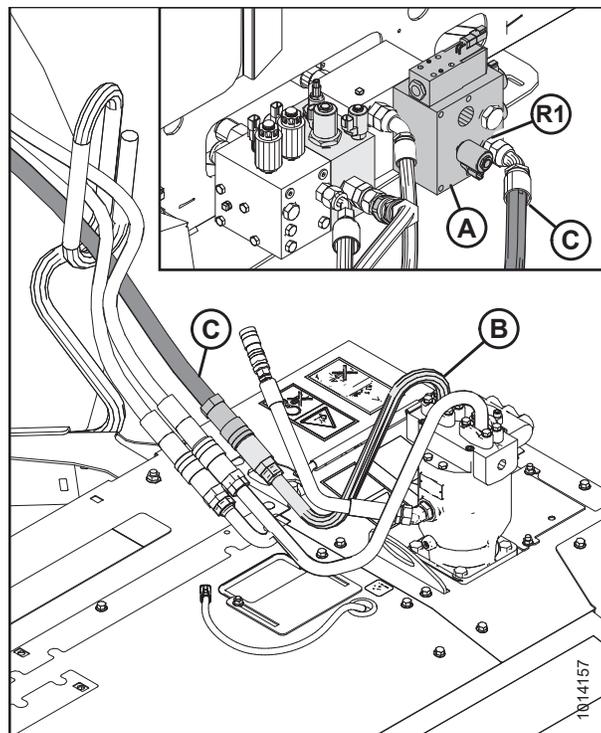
Соединения шлангов через блок реверса косилки
